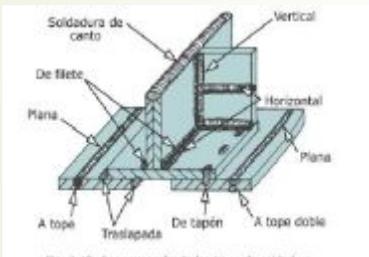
Denominación de los tipos de soldadura
